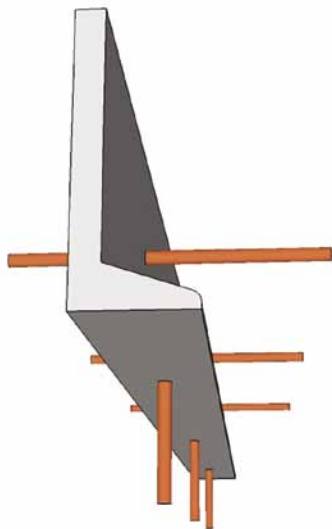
Установка шпилек для стандартного способа изоляции набора
